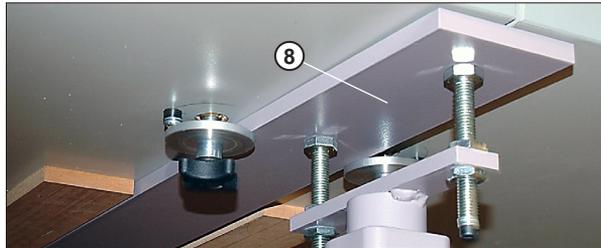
Tischplattenbefestigung an der Mittelstütze
